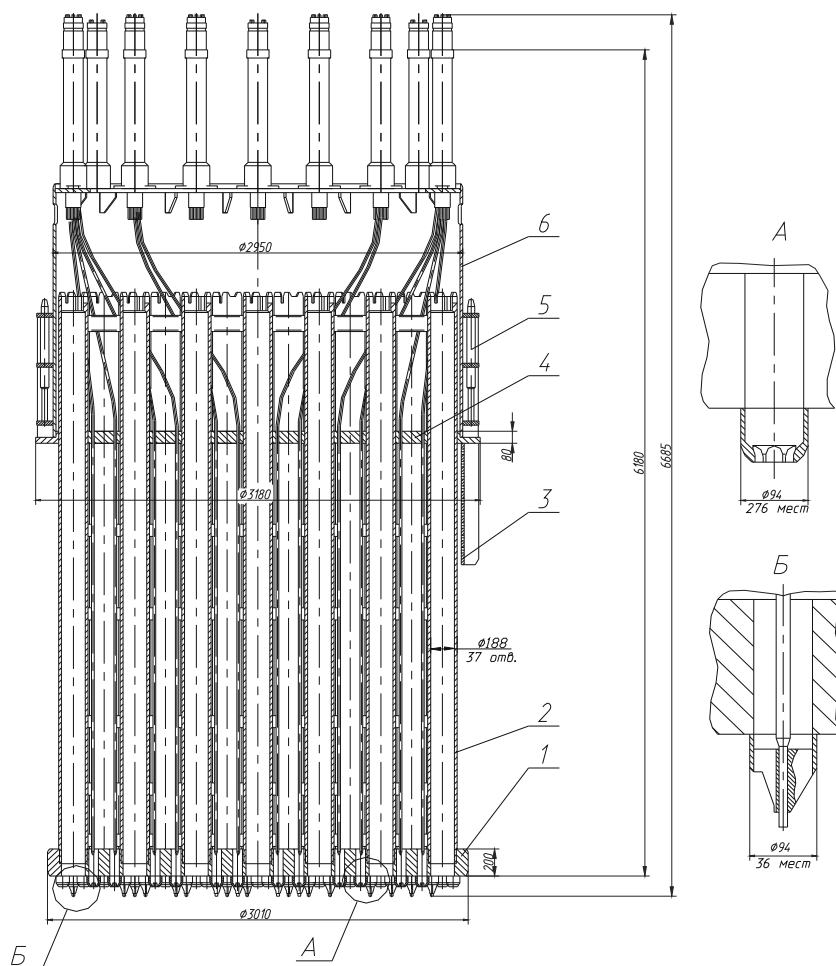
Общий вид блока защитных труб: 1 – нижняя плита; 2 – труба защитная; 3 – щит отбойный; 4 – верхняя плита; 5 – пружинный блок; 6 – обечайка
